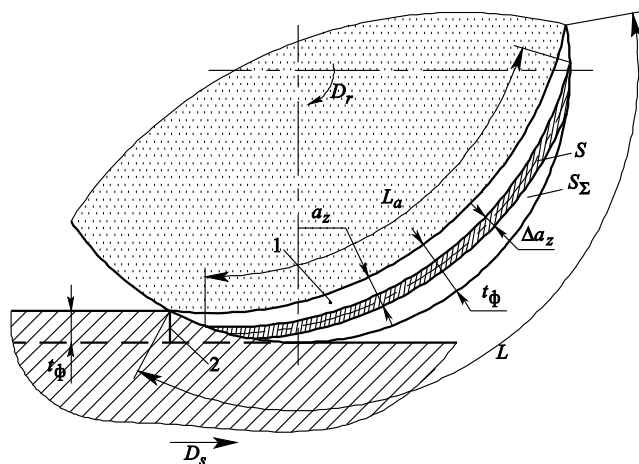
Схема взаимодействия шлифовального круга с заготовкой
